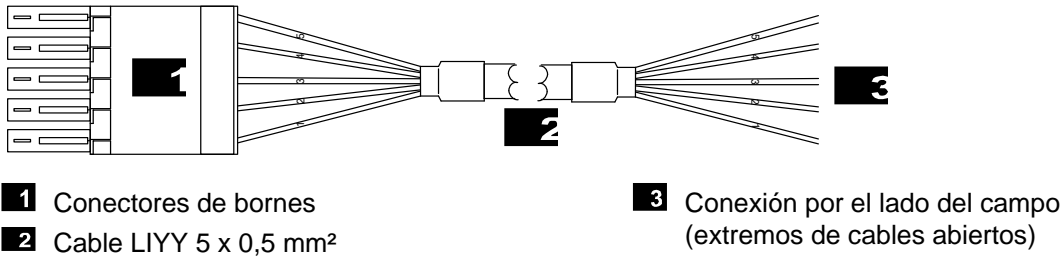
Cable del kit de cables de sistema X-CA 004 02
